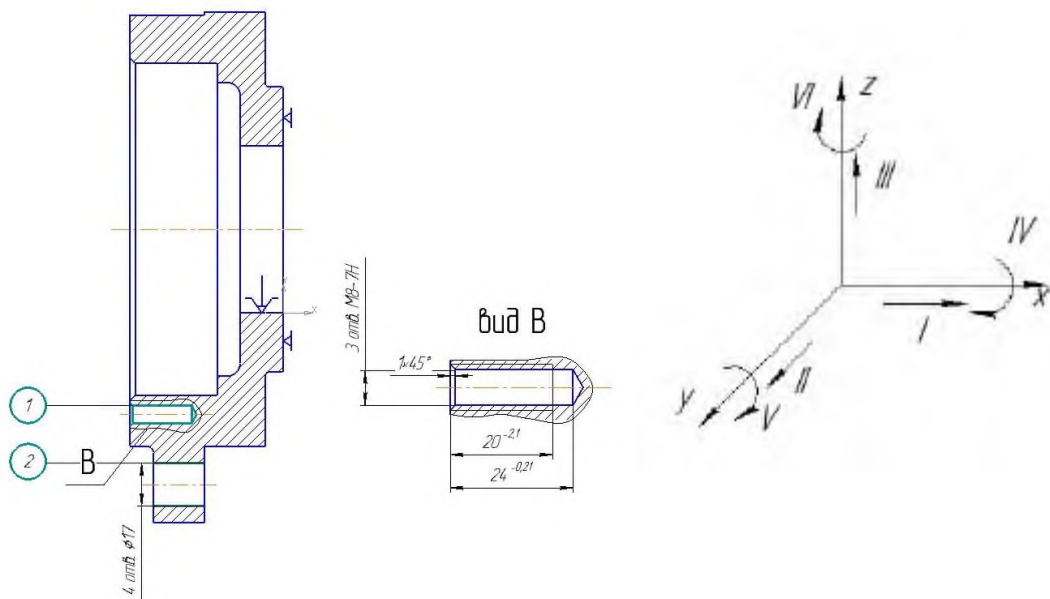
Перший спосіб базування та закріплення заготовки на операції 050
